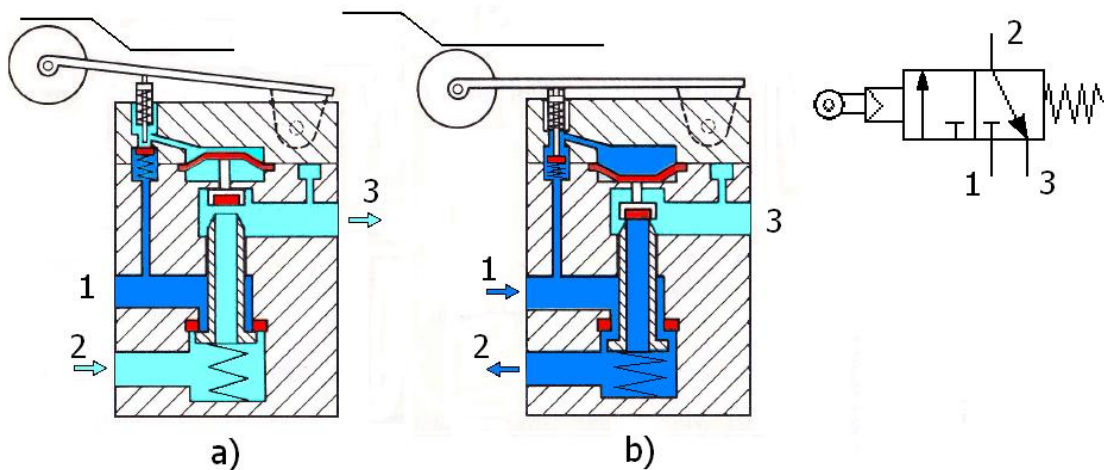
Ventil 3/2 přímo ovládaný kladkou [3]
